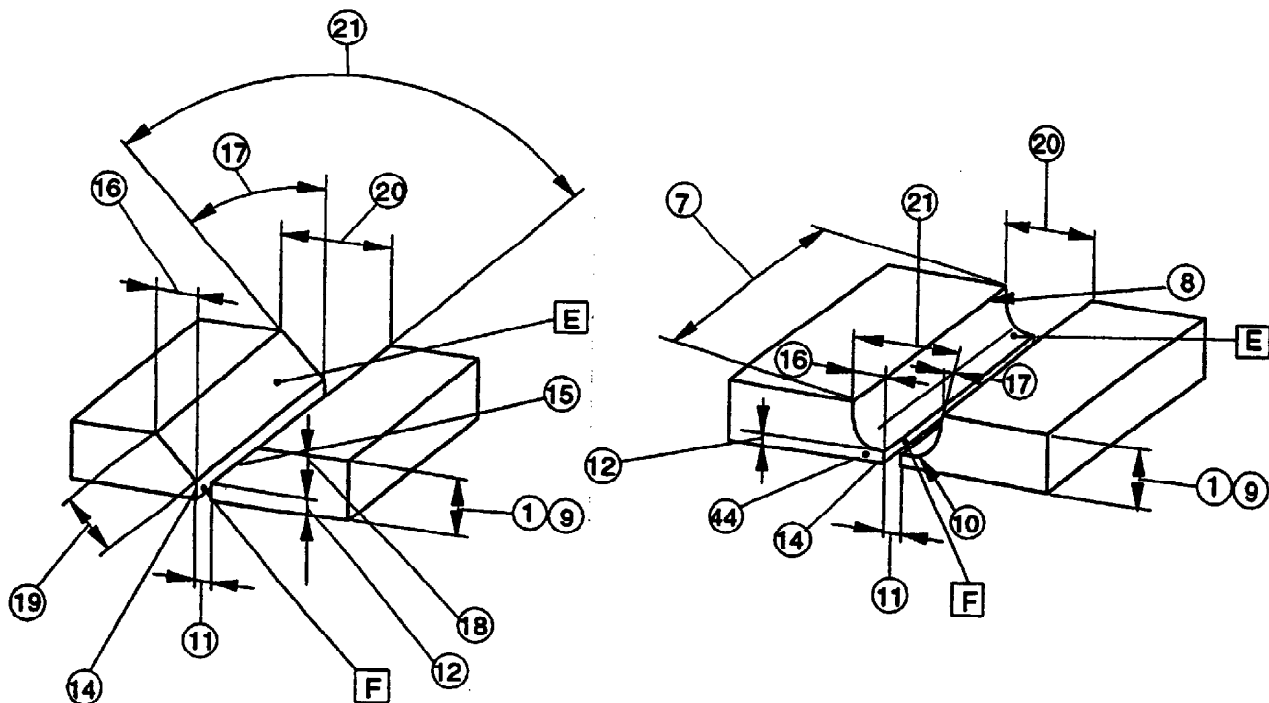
bis 8 beziehen sich auf Fugenvorbereitungen für das Schmelzschweißen, Bilder 9 bis 11 betreffen Formen für das Preßschweißen.
